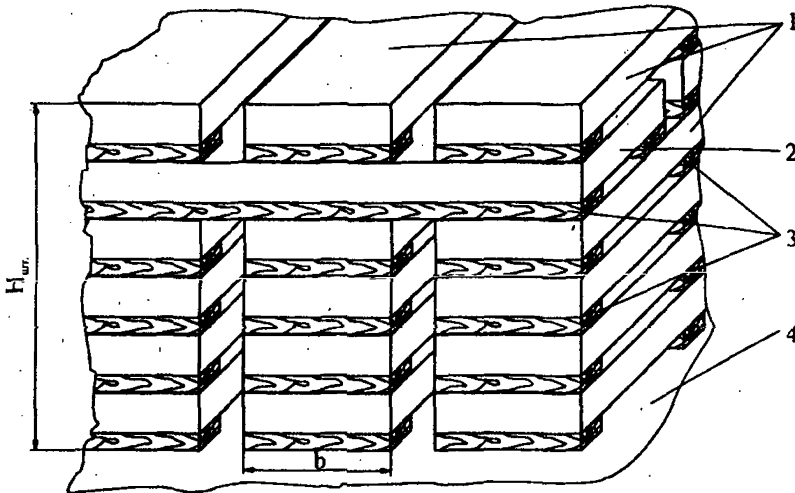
Схема укладки слитков прямоугольного сечения и слябов:
